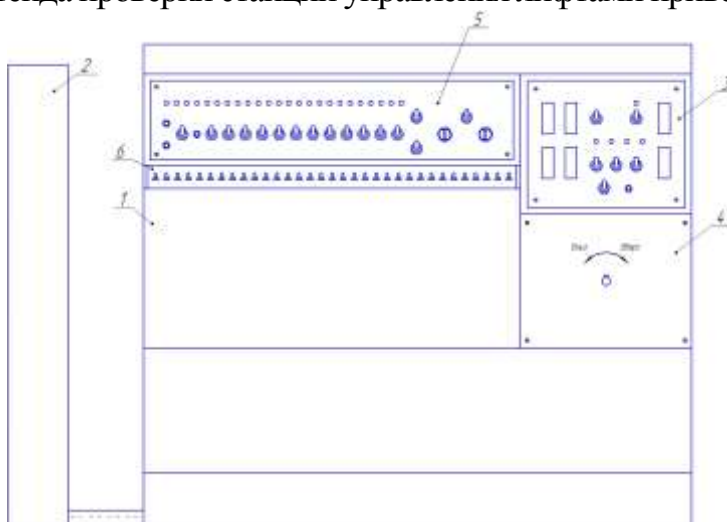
Общий вид стенда проверки станций управления лифтами
